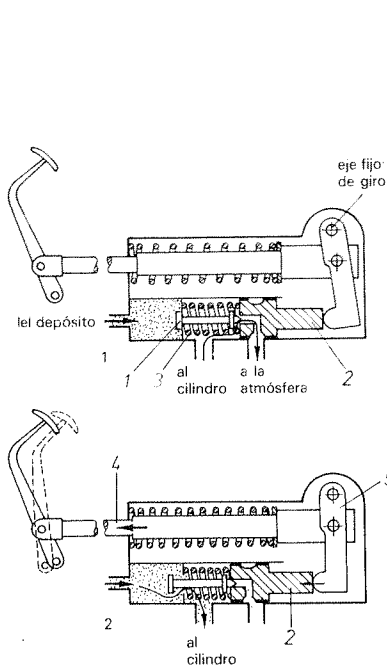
B Posiciones del servo-embrague: 1, embragado; 2, desembragado.
